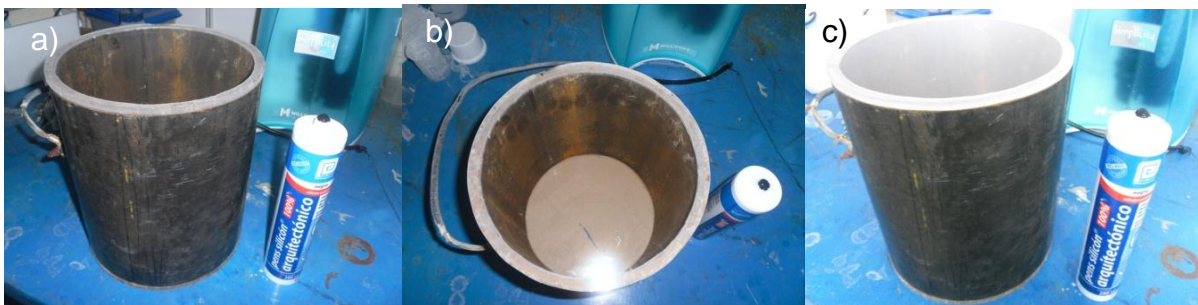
a) Ducto soldado y silicón, b) Sellado inferior, c) Sellado superior.
